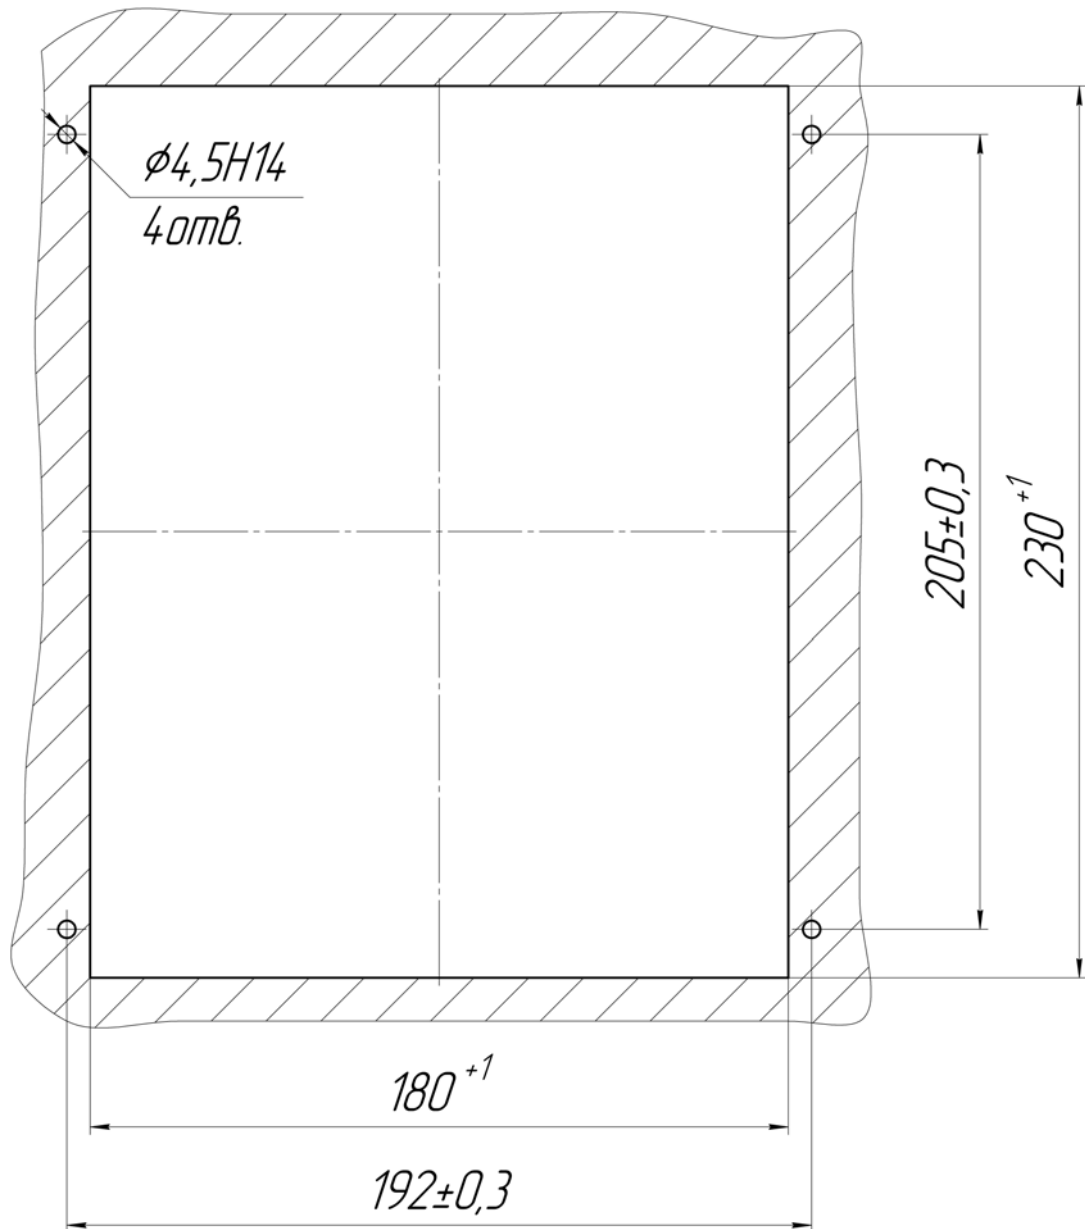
Габаритные размеры окна и крепежных отверстий для установки РТН-200-05.И1 ТН
